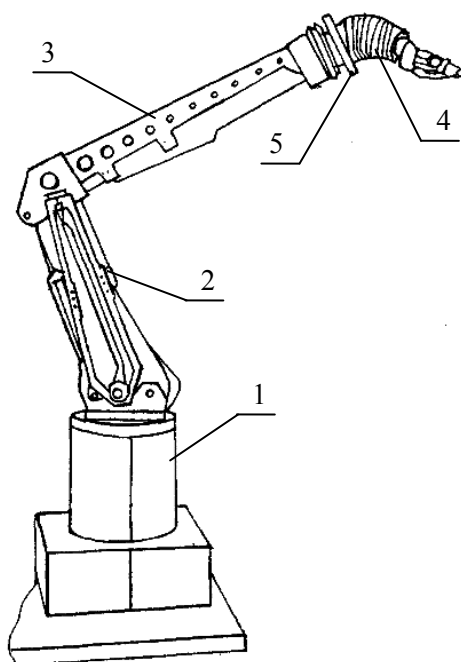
Схема промышленного робота «КОНТУР-002»: 1 – основание манипулятора с механизмом поворота; 2 – плечо с гидродвигателями; 3 – предплечье с распределительной плитой; 4 – кисть; 5 – рукоятка обучения
